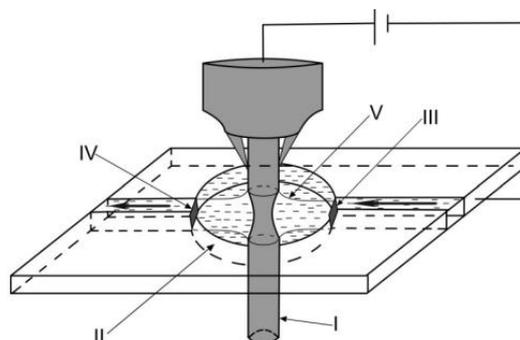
Схема обработки вольфрамовой заготовки в пленке электролита:
